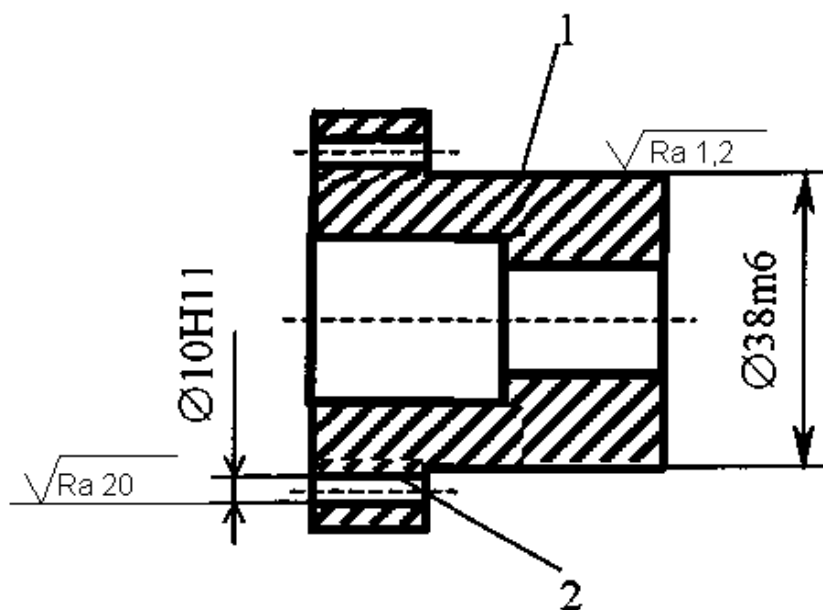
Эскиз детали с указанием заданных обозначений размеров и шероховатости поверхностей
